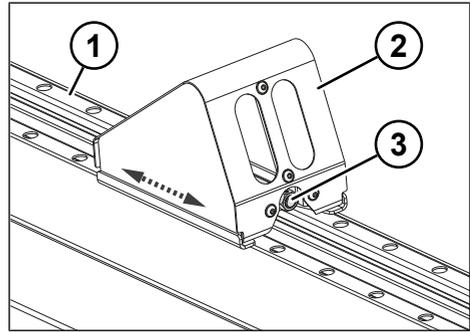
Regular a cunha de fixação de rolos de papel
